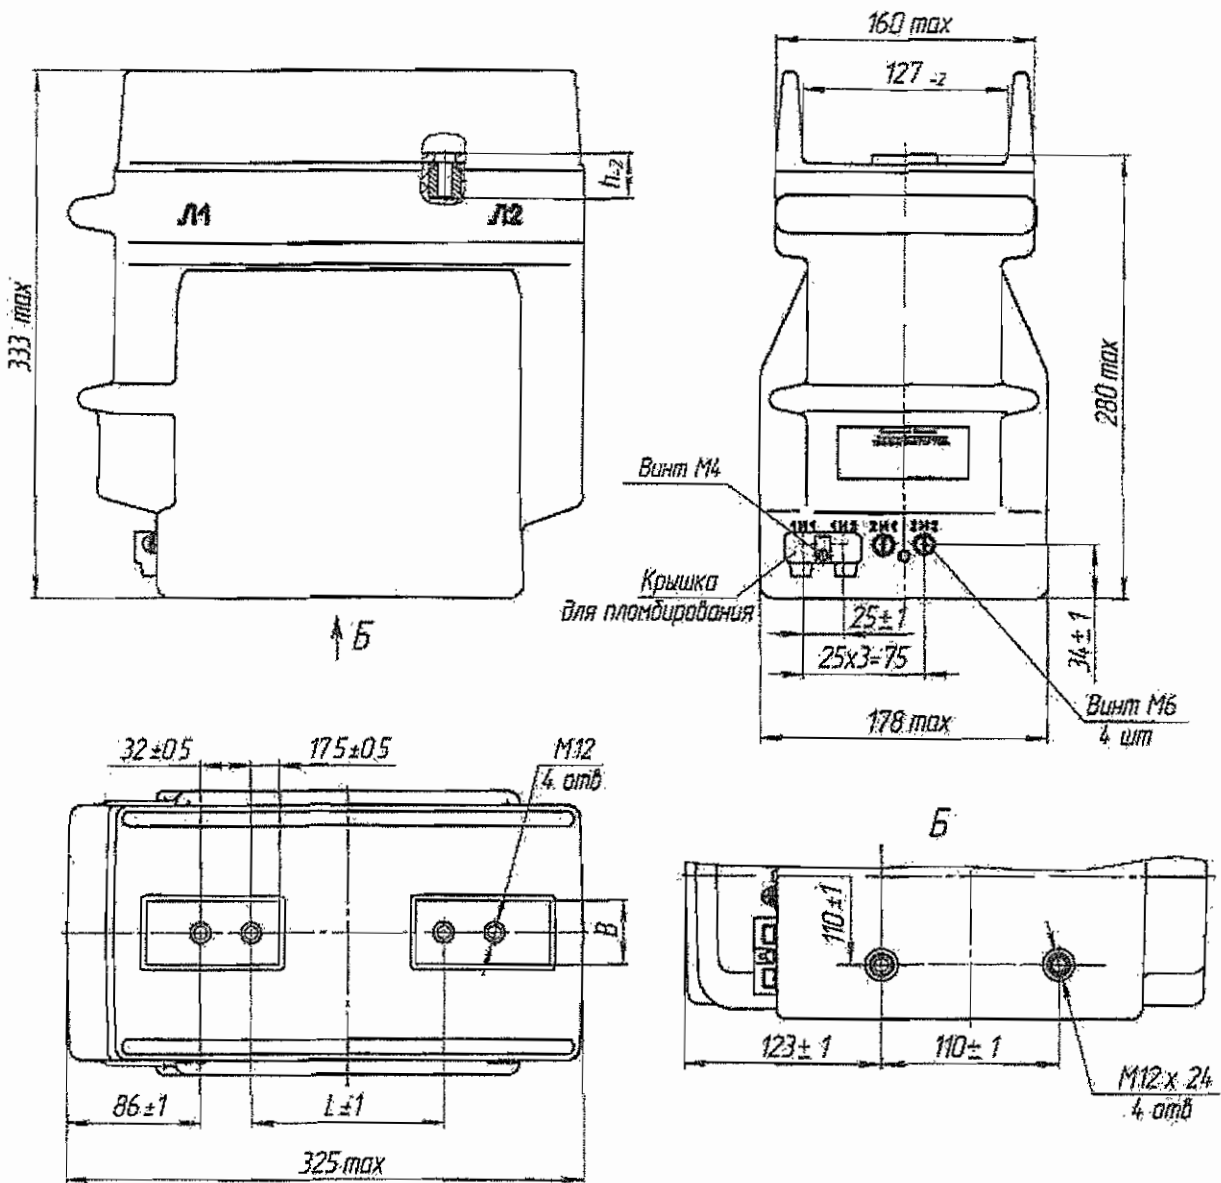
Общий вид и габаритные размеры трансформатора тока ТОЛ-20-2 на номинальные первичные токи 5-2000 А
